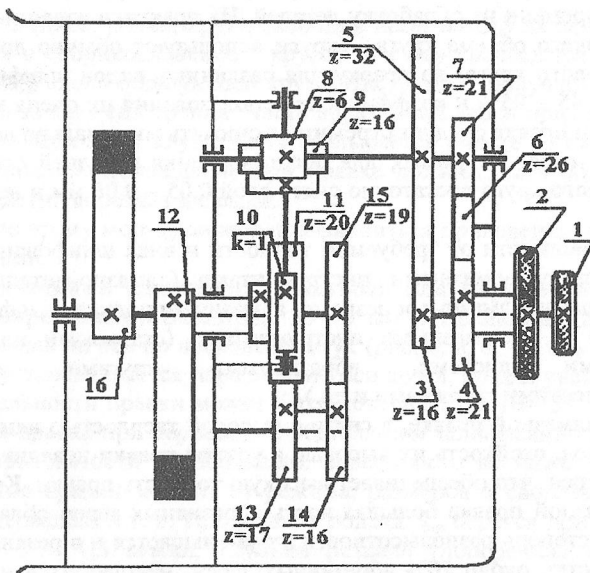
Кинематическая схема устройства для динамической балансировки шлифовальных кругов.
